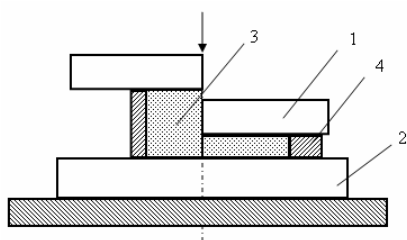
Схема прессования порошков труднодеформируемых материалов в условиях сдвиговых деформаций: 1 – верхний боёк; 2 – нижний боёк; 3 – уплотняемый порошок; 4 – кольцевая деформируемая обойма [9]
